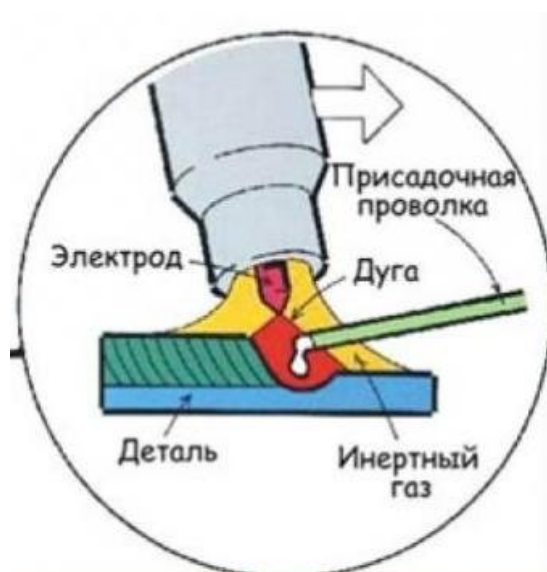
Схема аргодуговой сварки неплавящимся электродом
